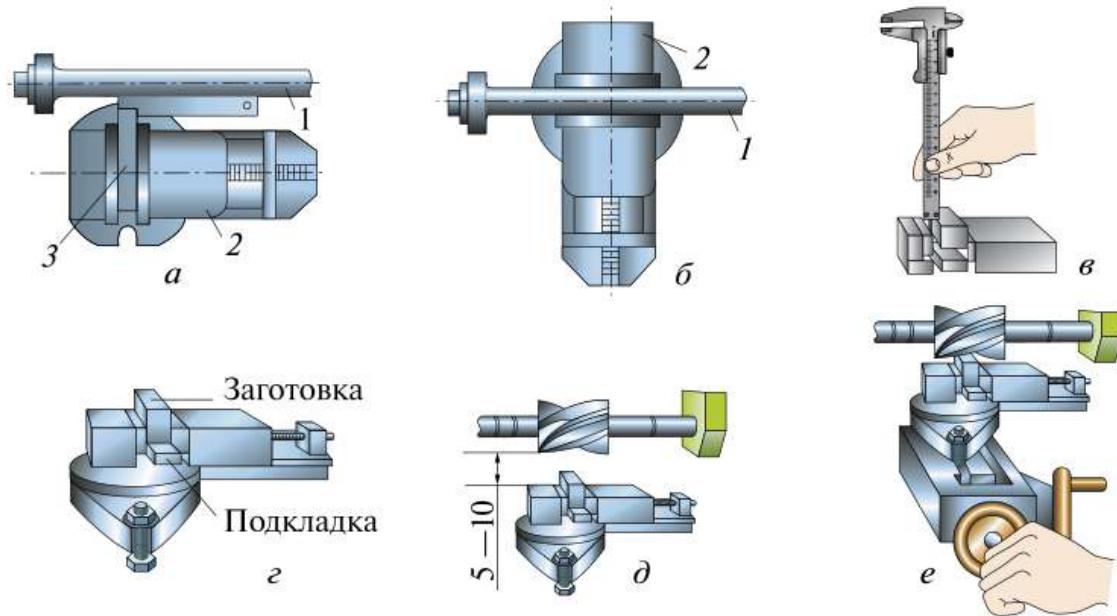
Последовательность фрезерования плоских поверхностей:
